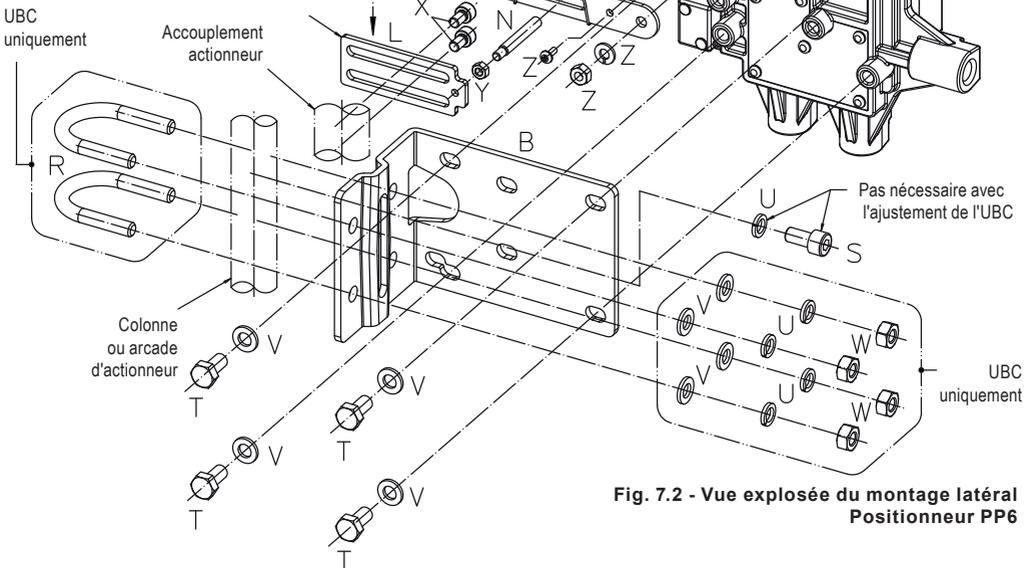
Vue explosée du montage latéral Positionneur PP6
